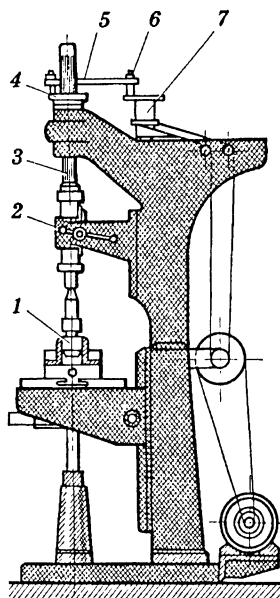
Сверлильный станок, приспособленный для притирки:
